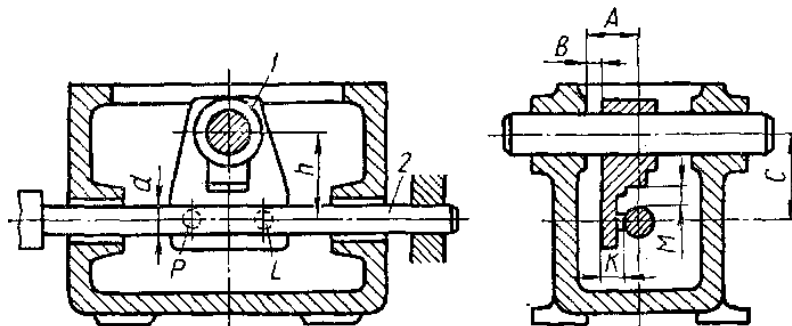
Вивірка положення заготівлі корпусної деталі на верстаті: 1 — пристосування для перевірки положення заготівлі та розточувальної скалки; 2 - розточувальна скалка.
